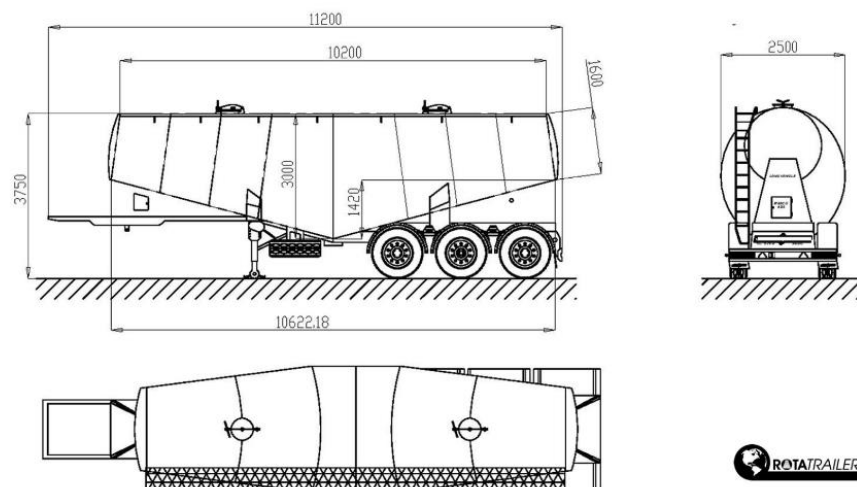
Напівпричіп борошновоз фірми Rota Trailer
